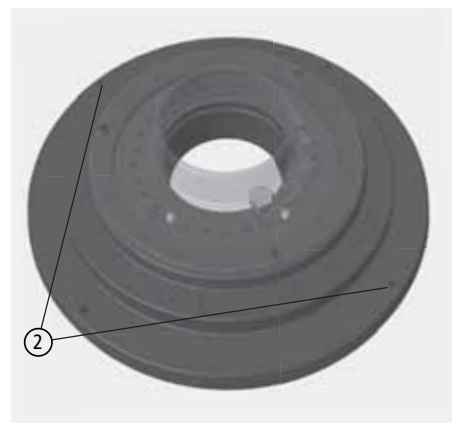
Bohrungen für Gewindestifte in Drehkonsole
